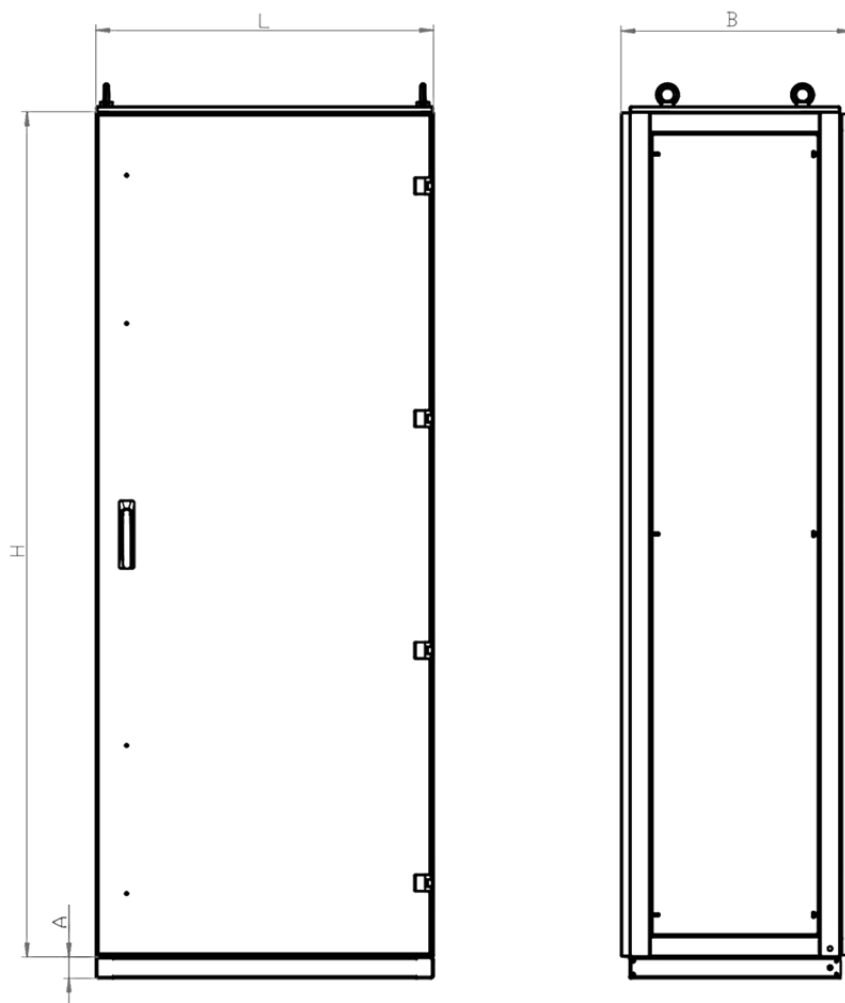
Габаритные размеры шкафов ШРЗА
